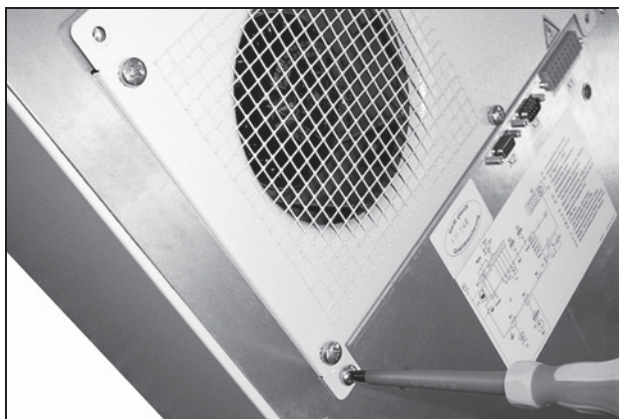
Befestigungsschrauben für die Abdeckung mit Ventilator entfernen
